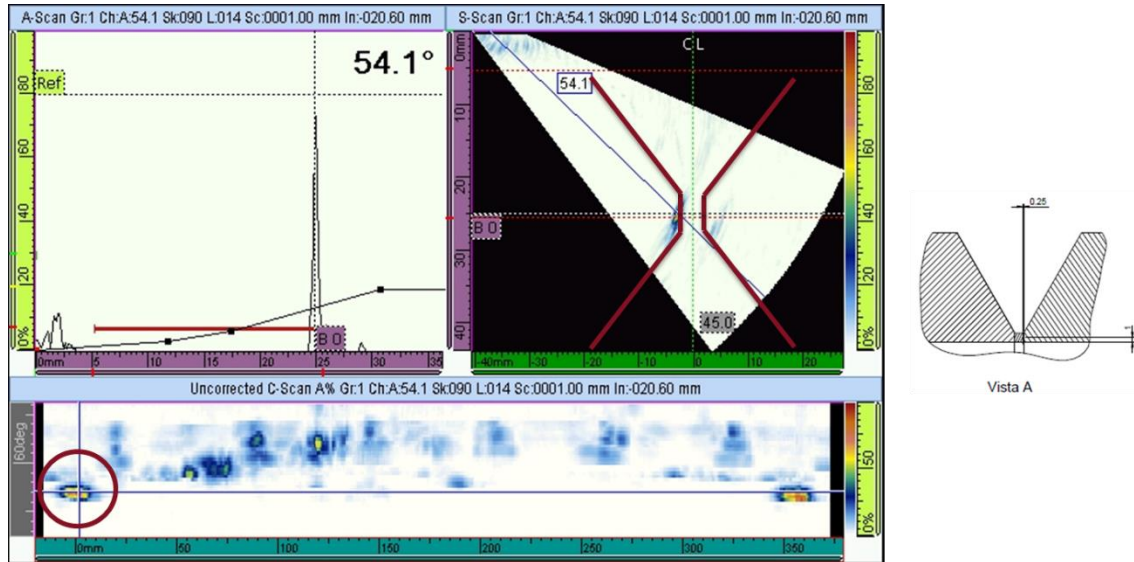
Inspeção da descontinuidade na raiz da soldadura do *mockup* END-01.
